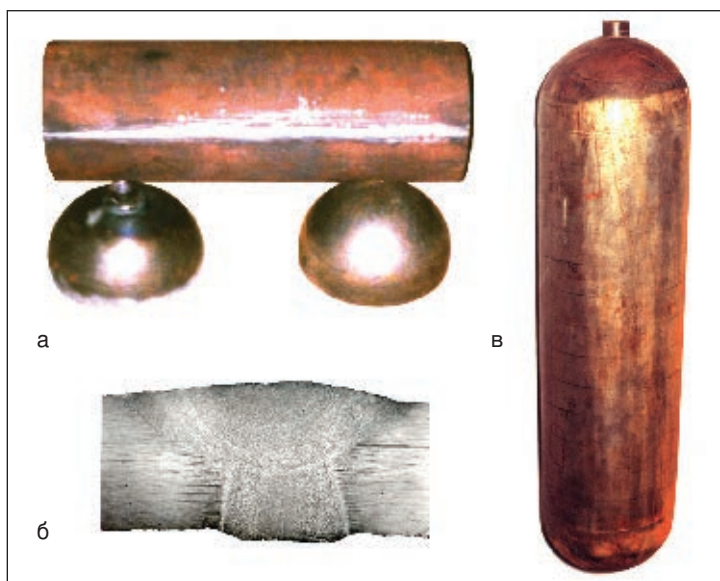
Заготовки и корпуса сварного баллона: а — заготовки обечаек и днищ; б — макрошлиф сварного шва; в — корпуса баллона после сварки и термообработки
